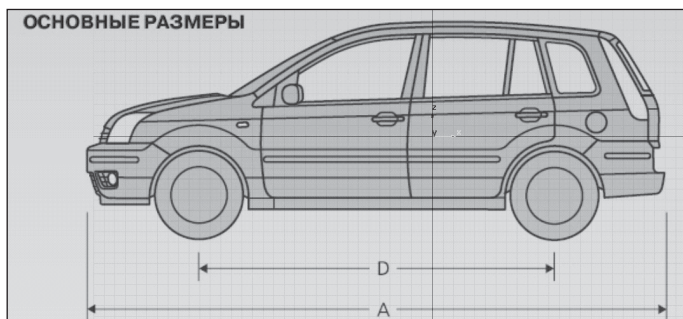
Эскиз автомобиля Ford Fusion (вид сбоку)
